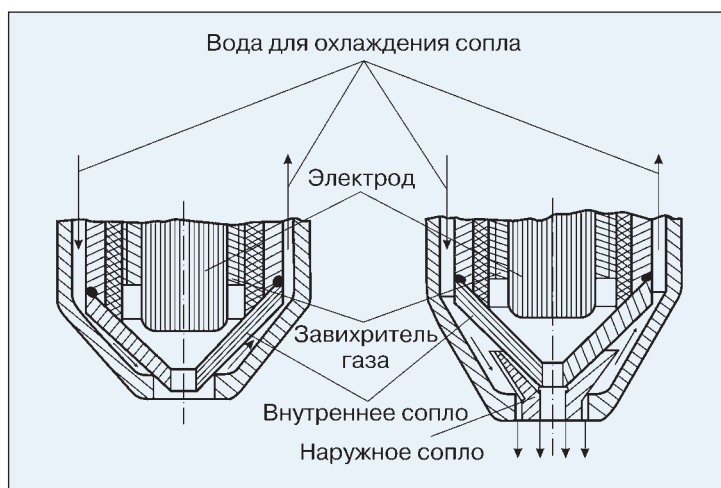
Схема головки плазмотрона: а — для обычной плазменной резки; б — для плазменной резки с добавкой воды
